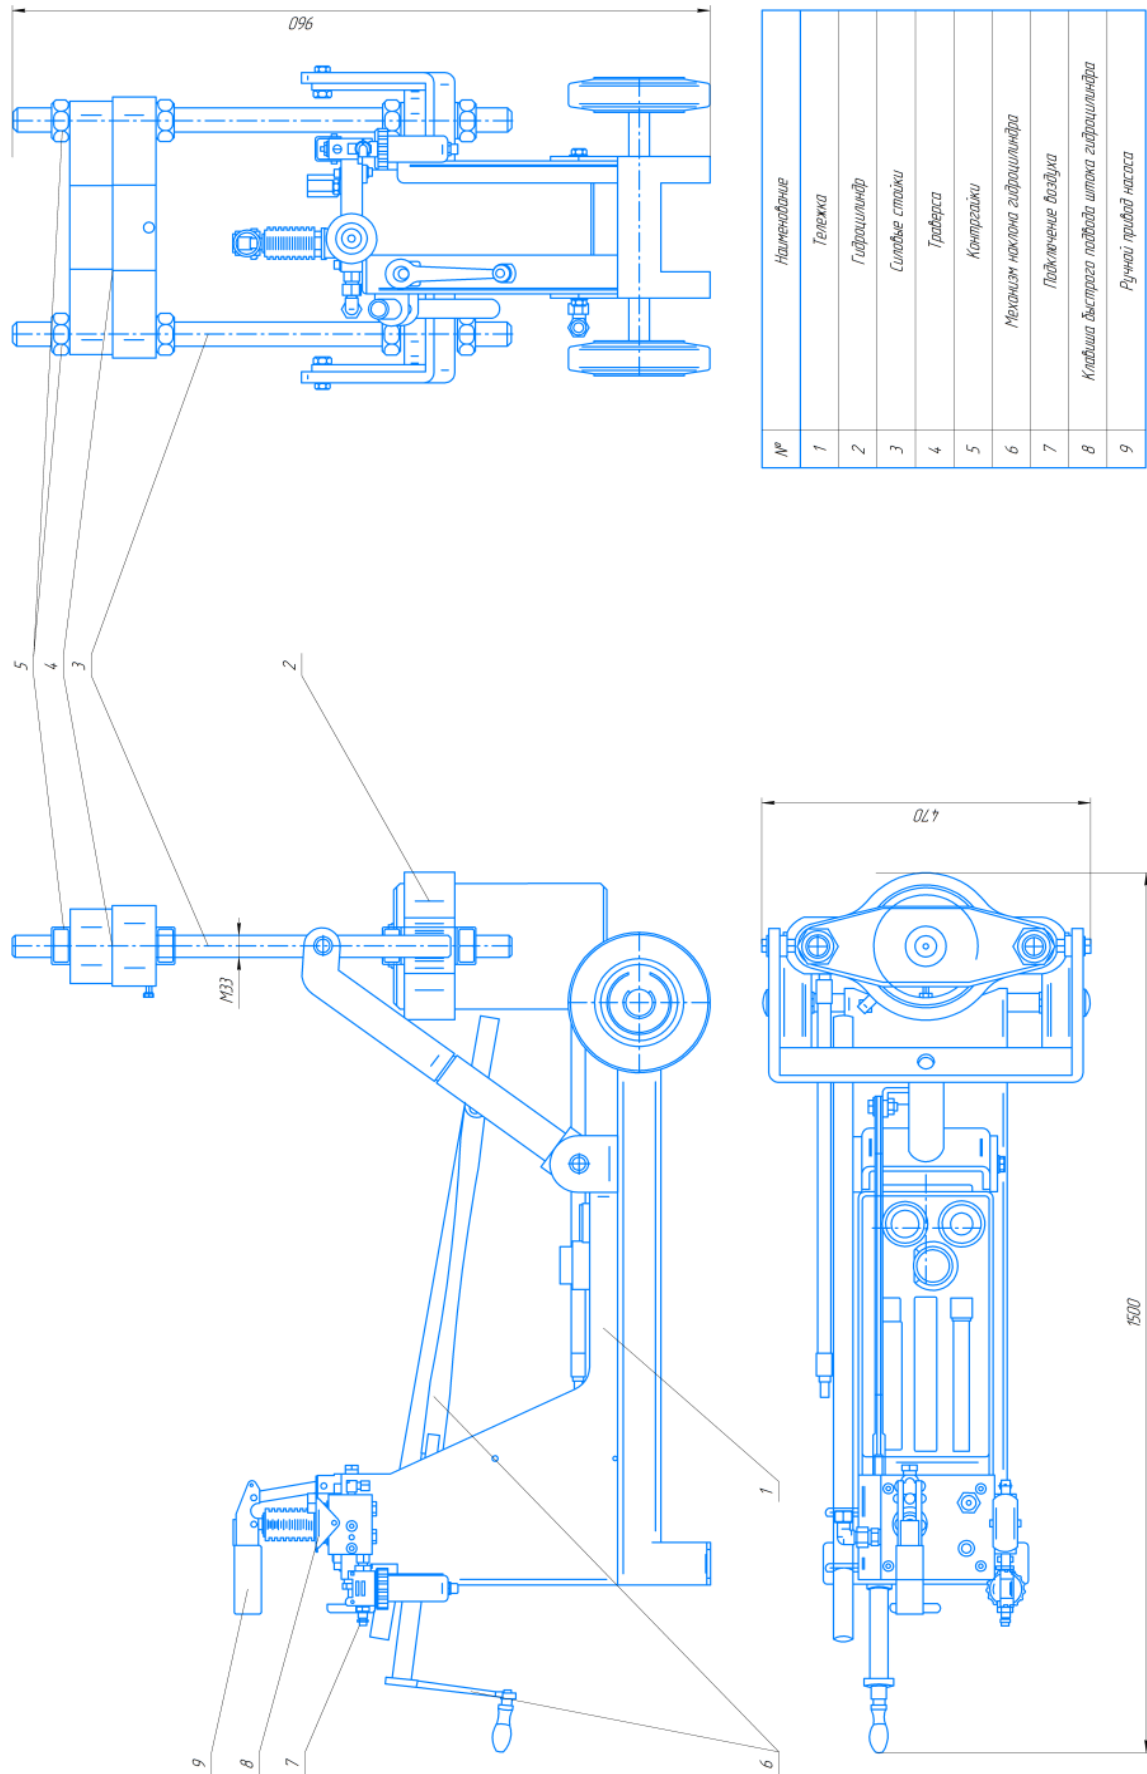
Стенд для выпрессовки и запрессовки шкворней.
